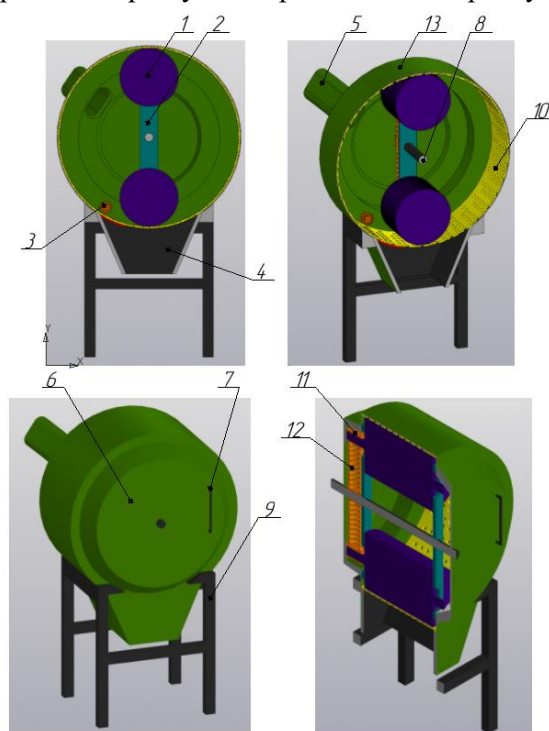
Конструкция пресс-гранулятора с подводом пара и устройством регулирования силы прижатия ролика к материалу: 1-ролик; 2-направляющая роликов; 3-форсунка для ввода пара; 4-разгрузочный патрубок; 5-загрузочное устройство; 6 – дверца; 7-ручка; 8-вал; 9-стойка; 10 – перфорированный барабан; 11-прижимная площадка; 12-пружина
